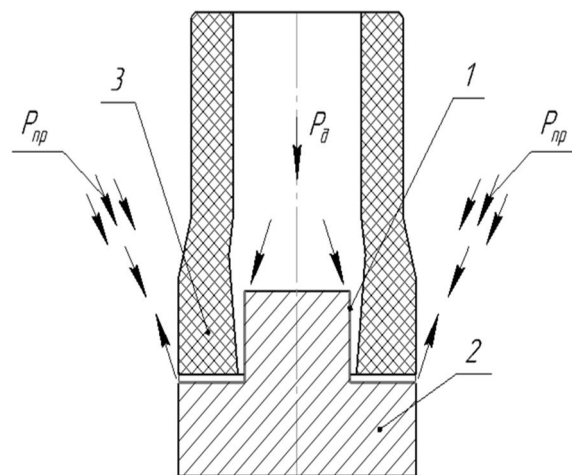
Схема формоутворення чистової обробки по зовнішньому контуру
